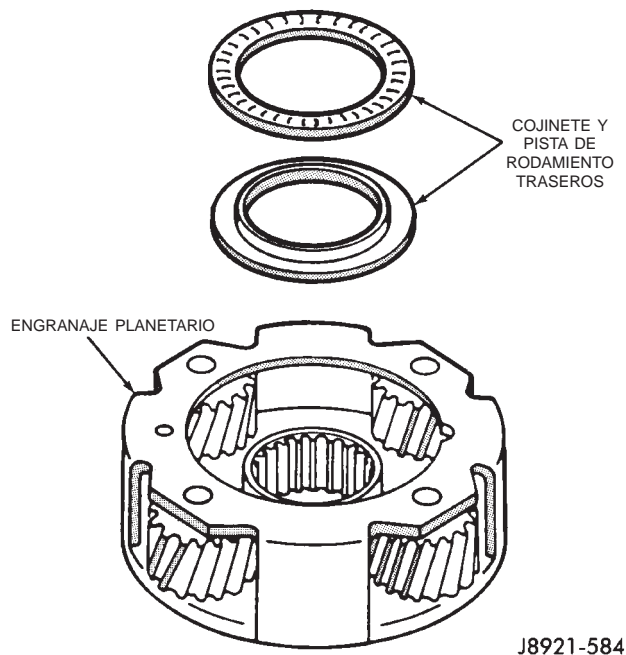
Instalación del cojinete y la pista de rodamiento traseros del engranaje planetario delantero
